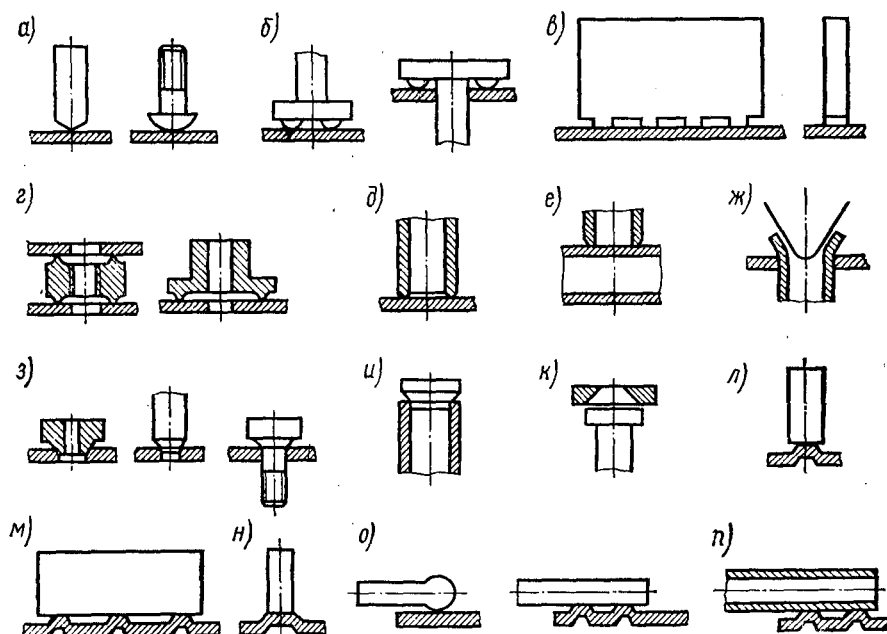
Схемы рельефных сварных соединений
